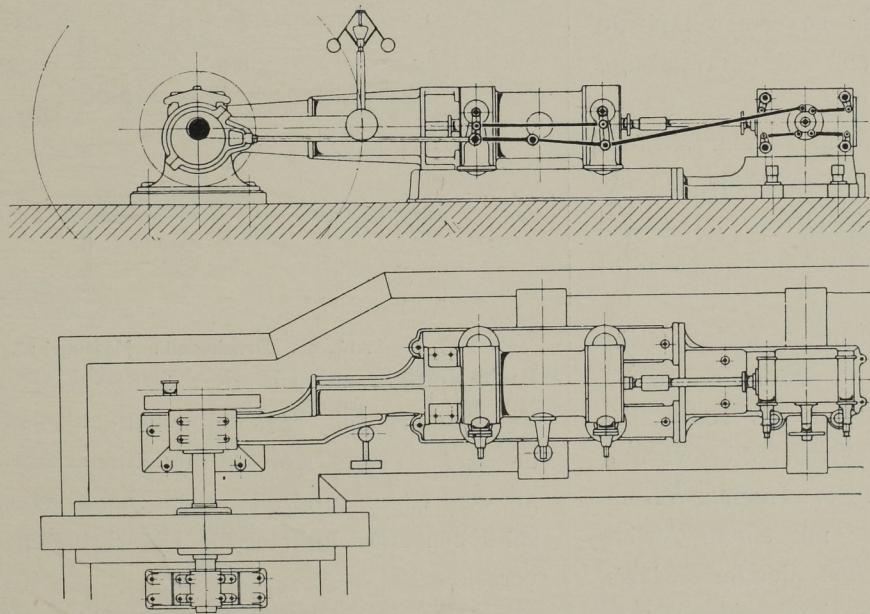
Seitenansicht und Grundriss. Massst. 1:80.
